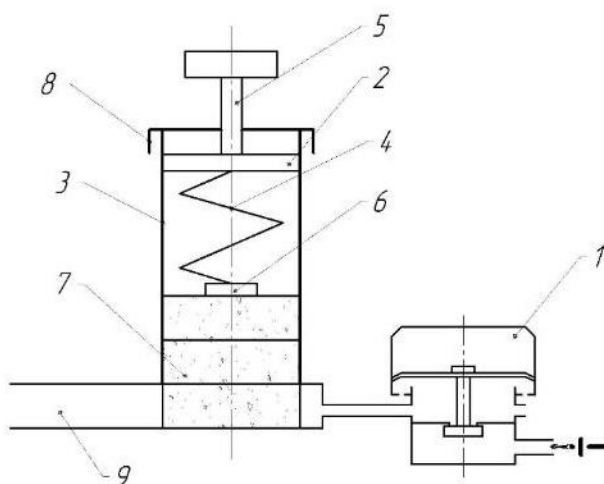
Схема пристрою автоматичної подачі пружних пробок: 1 - пульсатор; 2 - поршень; 3 - корпус; 4 - пружина; 5 - регулювальний гвинт; 6 - притискна пластина; 7 - пружні пробки; 8 - кришка; 9 - молокопровід
